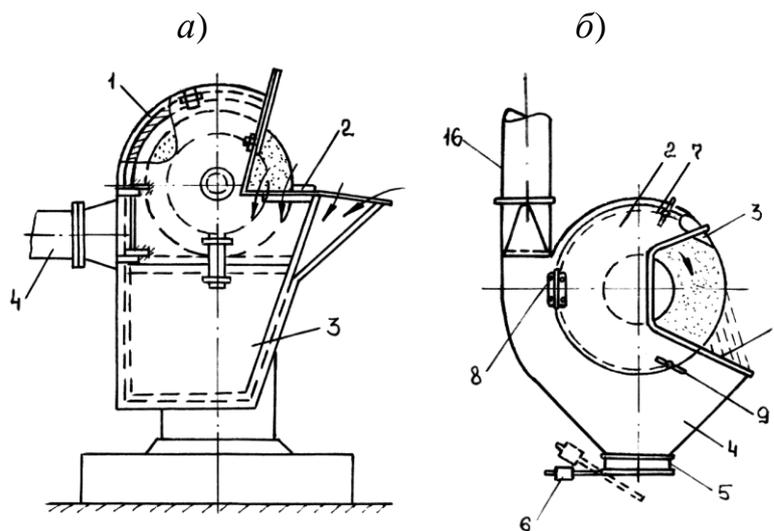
Кожухи-пылеприёмники: *а* – для заточного станка; *б* – для шлифовального или полировального кругов.
